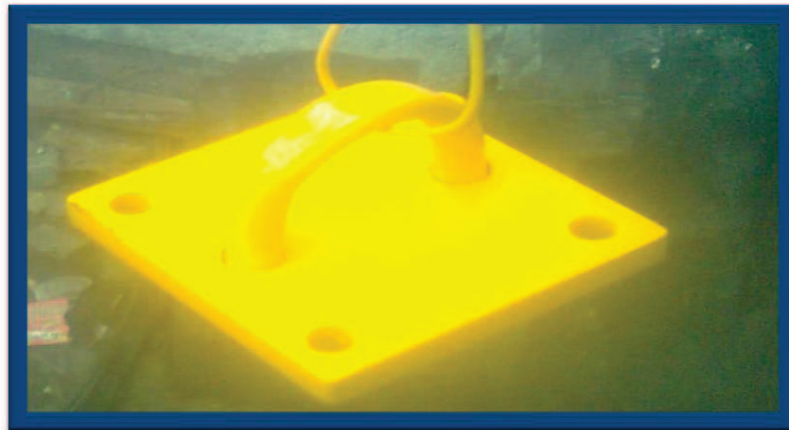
Eslinga para la caja de engranajes del motor J-33 terminada
